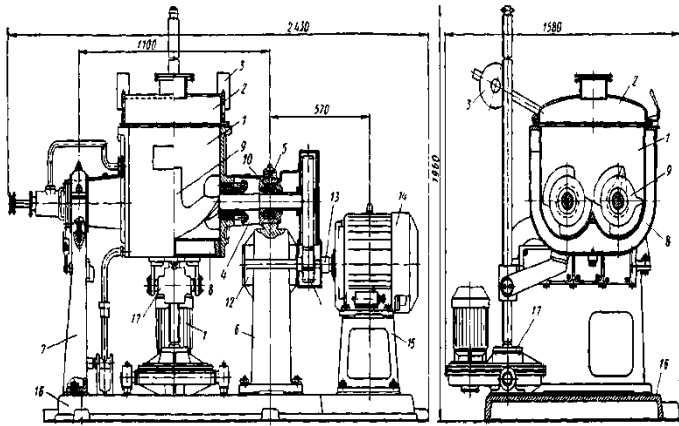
Загальний вигляд змішувача із Z-подібними лопатями: 1 – корпус; 2 – кришка корпусу; 3 – протизваги; 4 – цапфа; 5 – підшипник ковзання; 6, 7 – опорні стояки; 8 – теплообмінна сорочка; 9 – ротор із Z-подібними лопатями; 10 – підшипник кочення; 11 – зубчаста передача; 12 – редуктор привода; 13 – муфта; 14 – електродвигун; 15 – опора електродвигуна; 16 – фундаментна плита; 17 – механізм розвантаження
